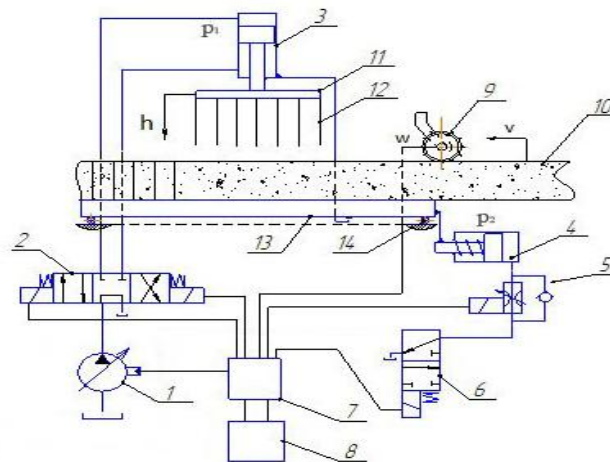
Гідравлічна схема автоматизованого пристрою для формування заготовок цегли
